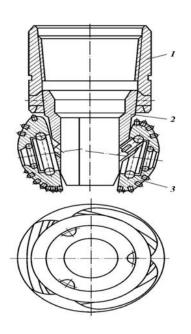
Схема устройства бурильной головки режущего действия типа MC3: 1 – корпус; 2 – шарошка; 3 – ось съемная
